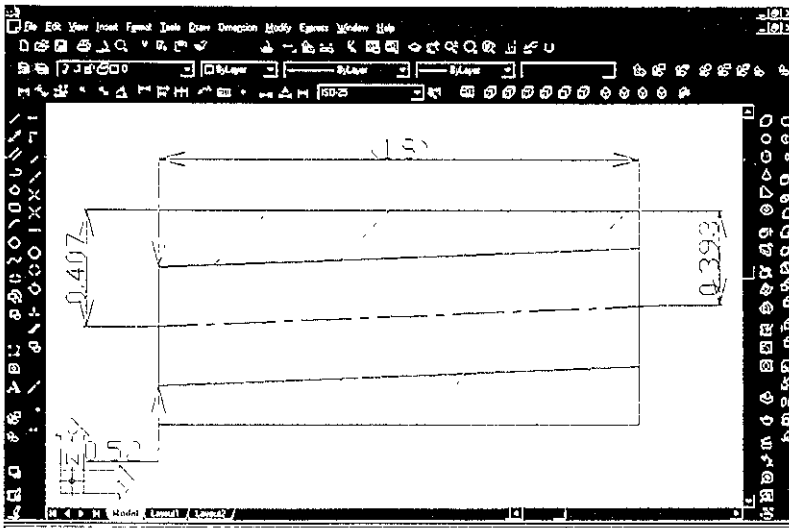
Placa barrenada interiormente que cumple con las tolerancias Rectangulares.
